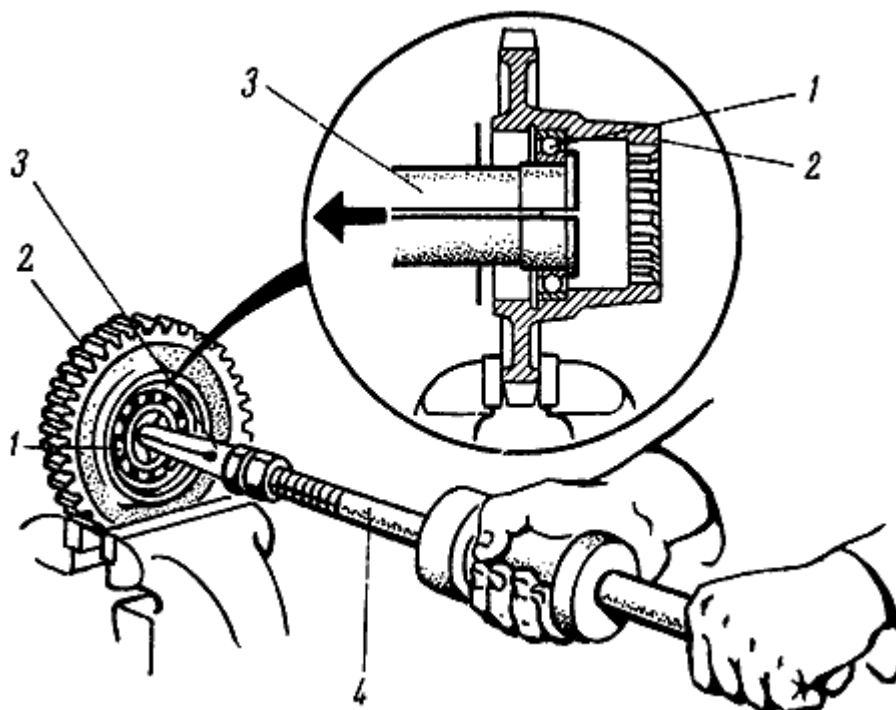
Выпрессовка подшипника из ведомой шестерни II ступени привода ВОМ:
